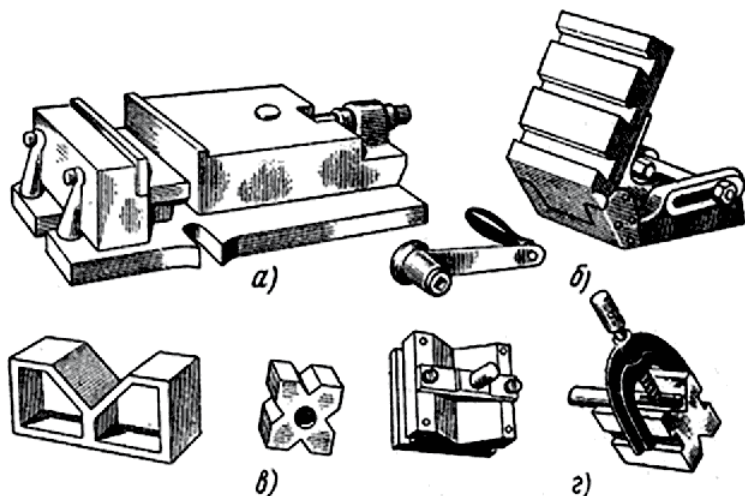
Приспособления для закрепления изделий на станке при сверлении:
